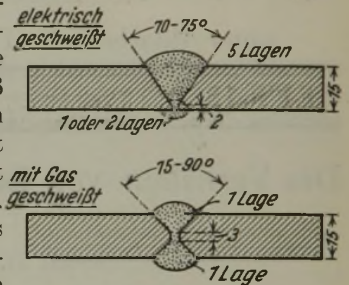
Form der Schweißnähte für die elektrisch geschweißte und die mit Gas geschweißte Trommel.
